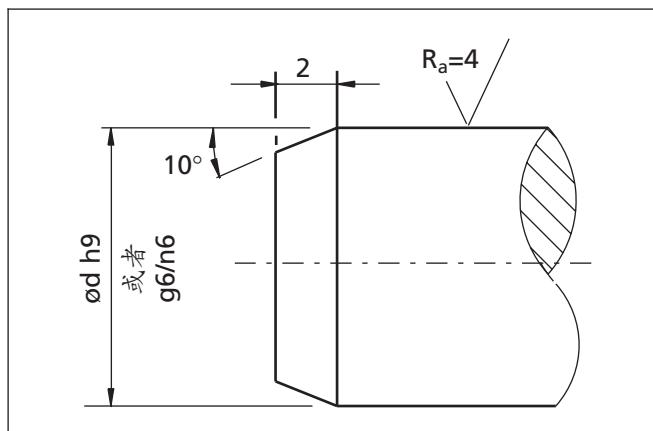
轴的公差、表面粗糙度和轴的倒角
